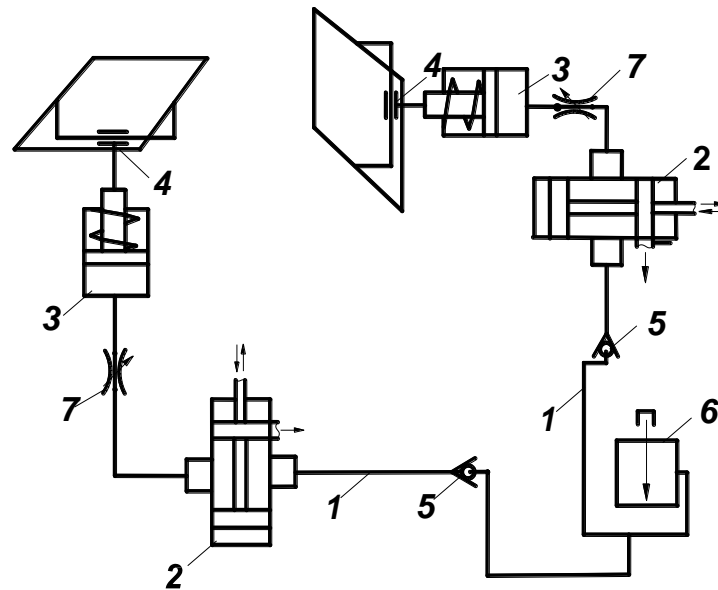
Принципова схема пневмоприводу для здійснення автоматизованої фрикційної обтяжки заготовки верху.
